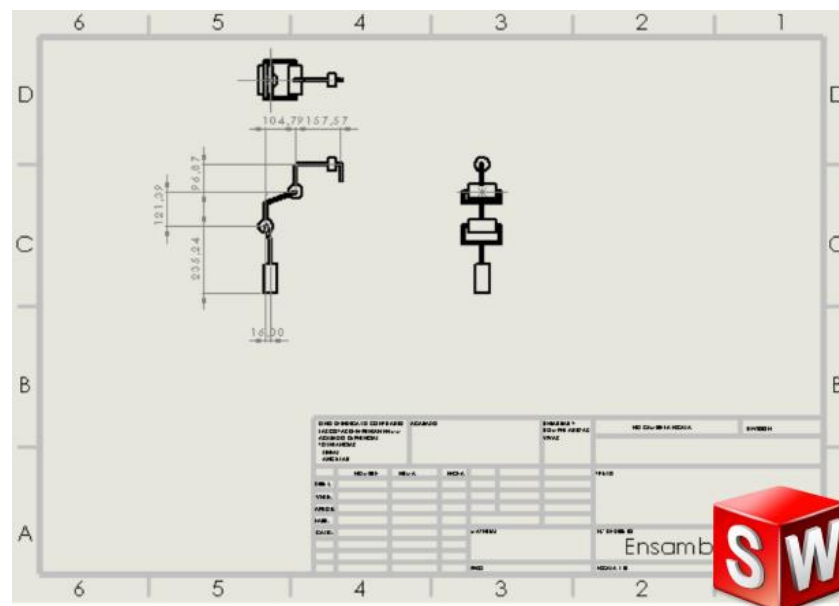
Esquema general de Diseño. Fuente:(Propia).
